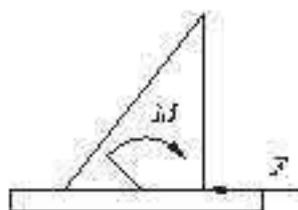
Схема нагружения сварного шва
